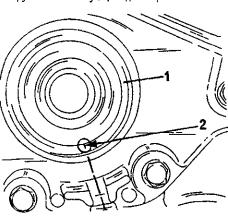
Установка переднего сальника коленчатого вала (1). Маркировка (2) должна располагаться по одной линии с цапфой.
